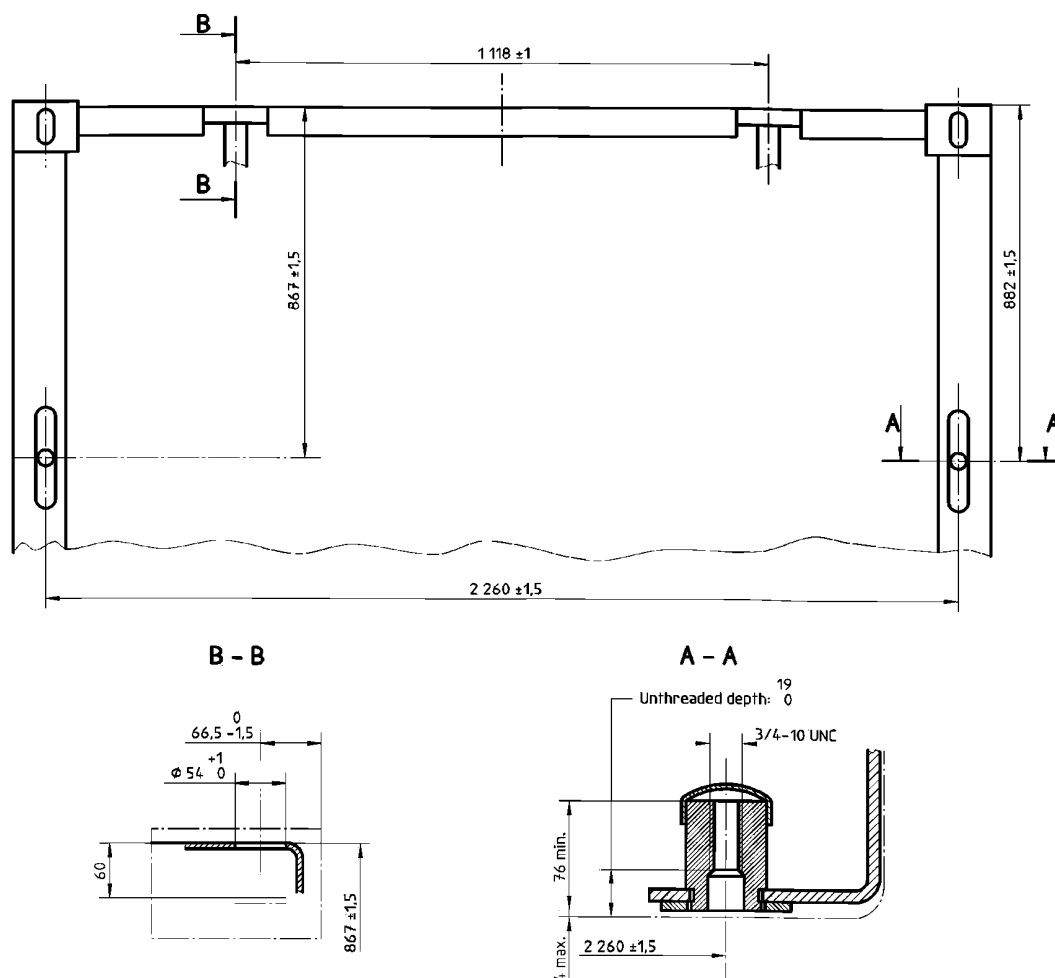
Расположение и размеры гнезд для крепления навесного генератора
